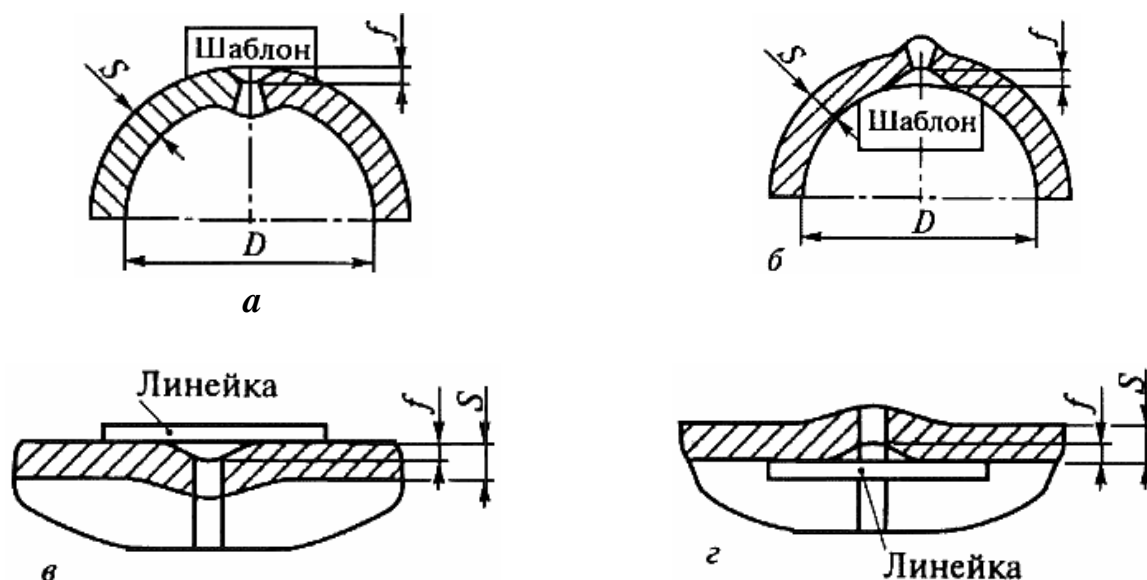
Контроль увода кромок продольных и кольцевых сварных соединений
